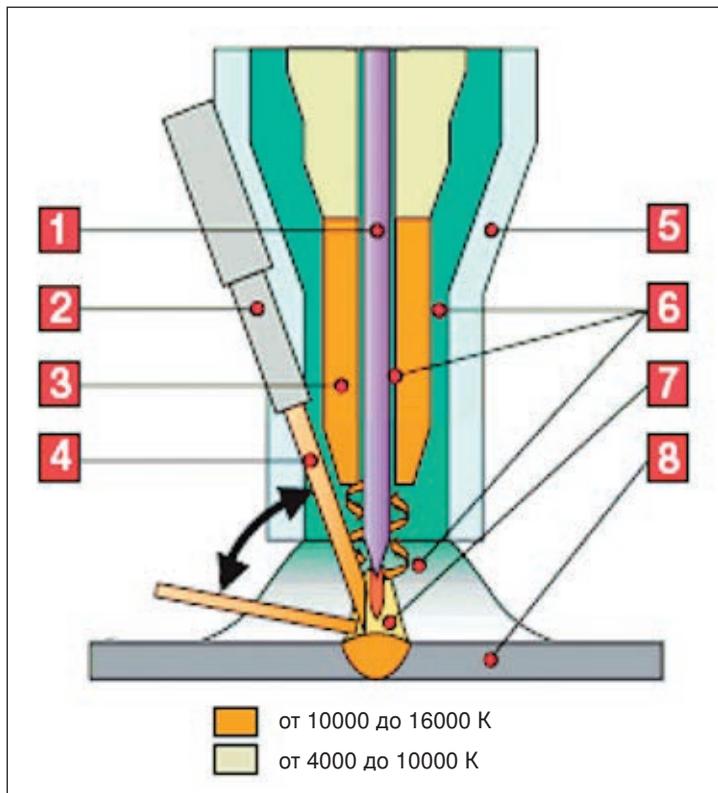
Схематическая конструкция горелки ТОРТIG: 1 — вольфрамовый электрод; 2 — направляющая проволоки; 3 — двухканальное сопло; 4 — сварочная проволока; 5 — газовое сопло; 6 — защитный газ; 7 — электрическая дуга; 8 — изделие
